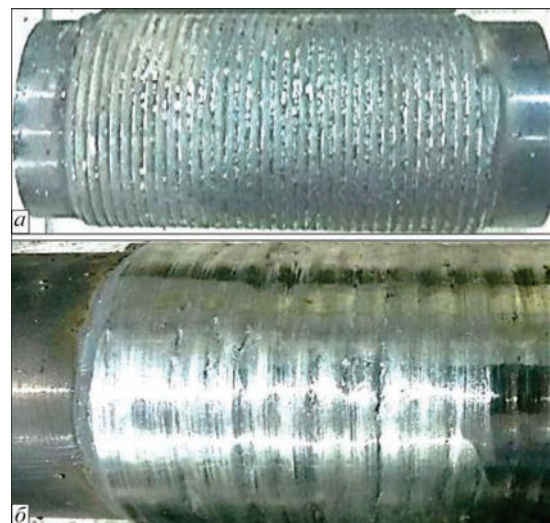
Внешний вид наплавленной поверхности валика диаметром 70 мм с неравномерным усилением наплавленных валиков и недостаточным перекрытием соседних валиков (514) непосредственно после наплавки (а) и после механической обработки (б)
